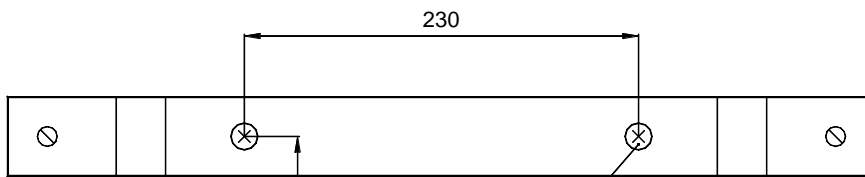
Вид корпуса СЛУП сзади и расположение монтажных отверстий
